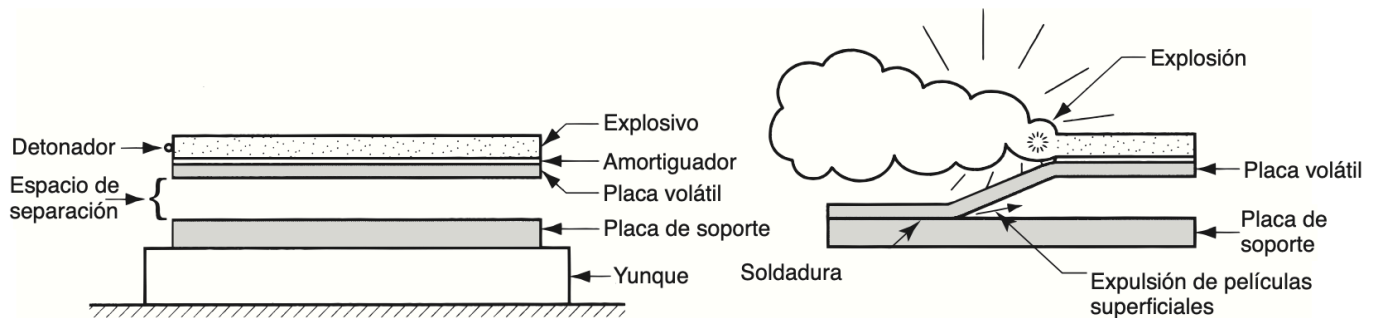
Proceso de soldadura por explosión. [27]
